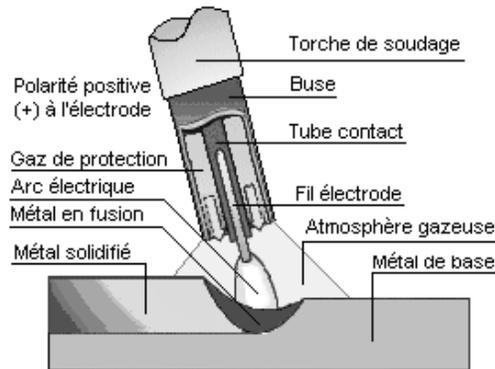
Soudage semi automatique sous protection gazeuse
